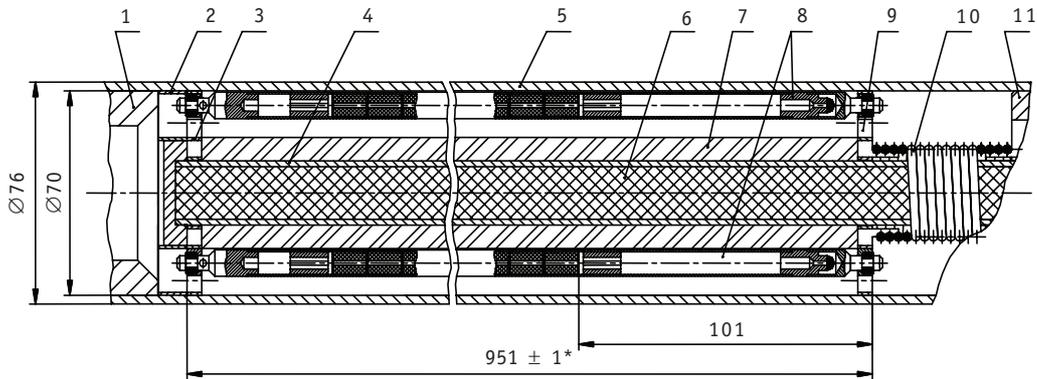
Продольный разрез ТК реактора ИВГ1.2М в районе активной зоны: 1 – втулка биологической защиты; 2 – нижняя опорная решетка; 3 – нижняя решетка; 4 – труба для установки поглотителя нейтронов; 5 – корпус ТК; 6 – поглотитель нейтронов; 7 – бериллиевый вытеснитель; 8 – твэл; 9 – верхняя опорная решетка; 10 – пружина; 11 – втулка упорная
